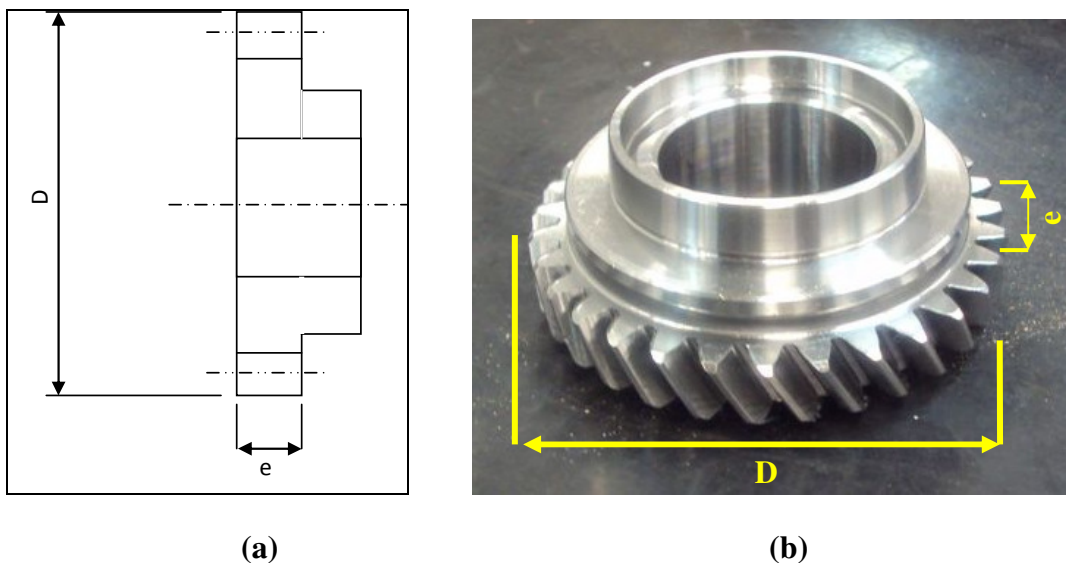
a) Croqui b) Foto de um exemplo de engrenagem
